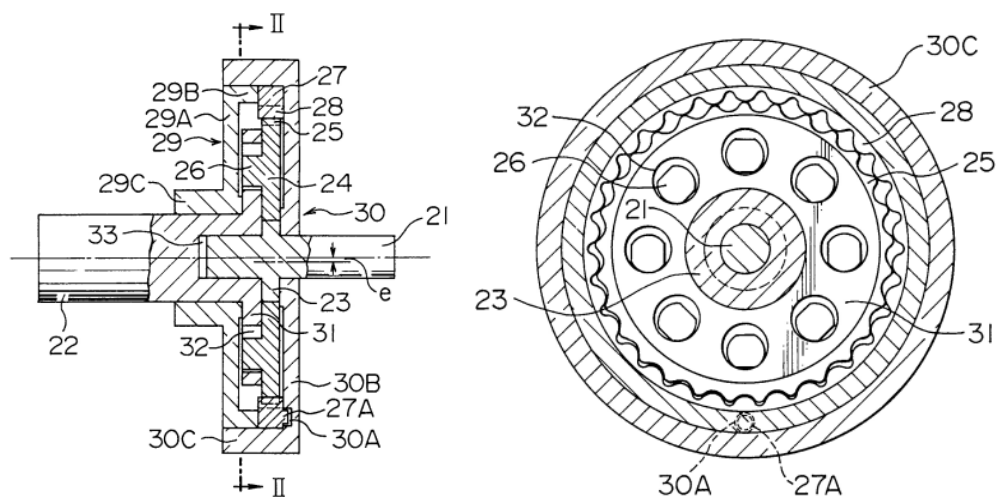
Епіциклоїдний планетарний редуктор Sumitomo Drive
